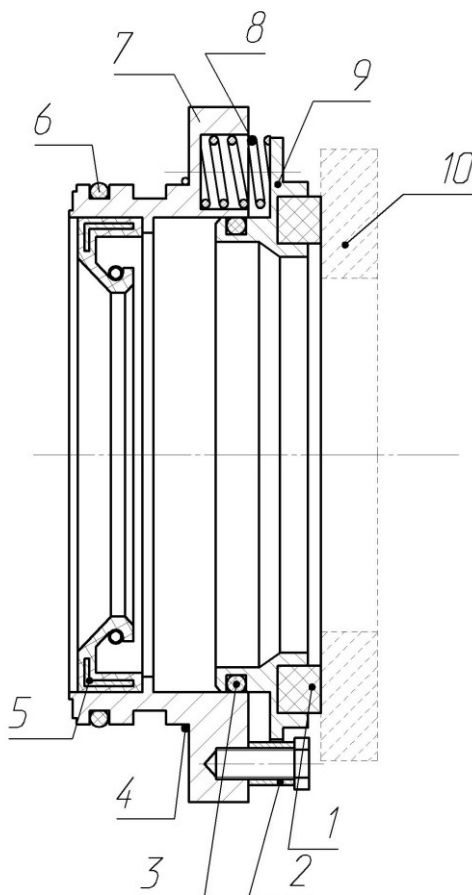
Уплотнение вала рабочего колеса пожарного насоса: 1 – кольцо антифрикционное; 2 – втулка упорная; 3, 4, 6 – кольцо резиновое уплотнительное; 5 – манжета резинокаркасная; 7 – втулка; 8 - пружина; 9 – кольцо подвижное; 10 - кольцо неподвижное.
